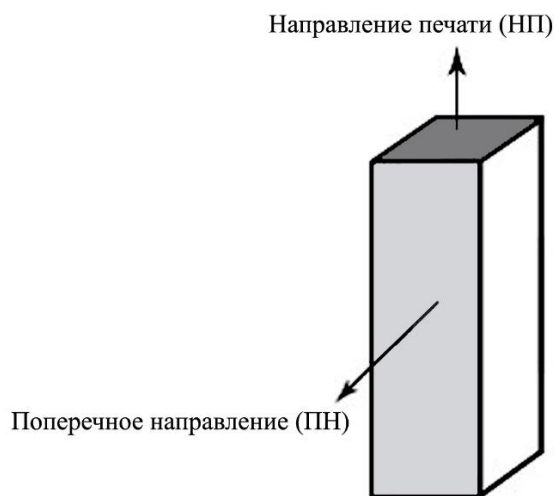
Схематическое обозначение плоскостей образцов и направлений печати
